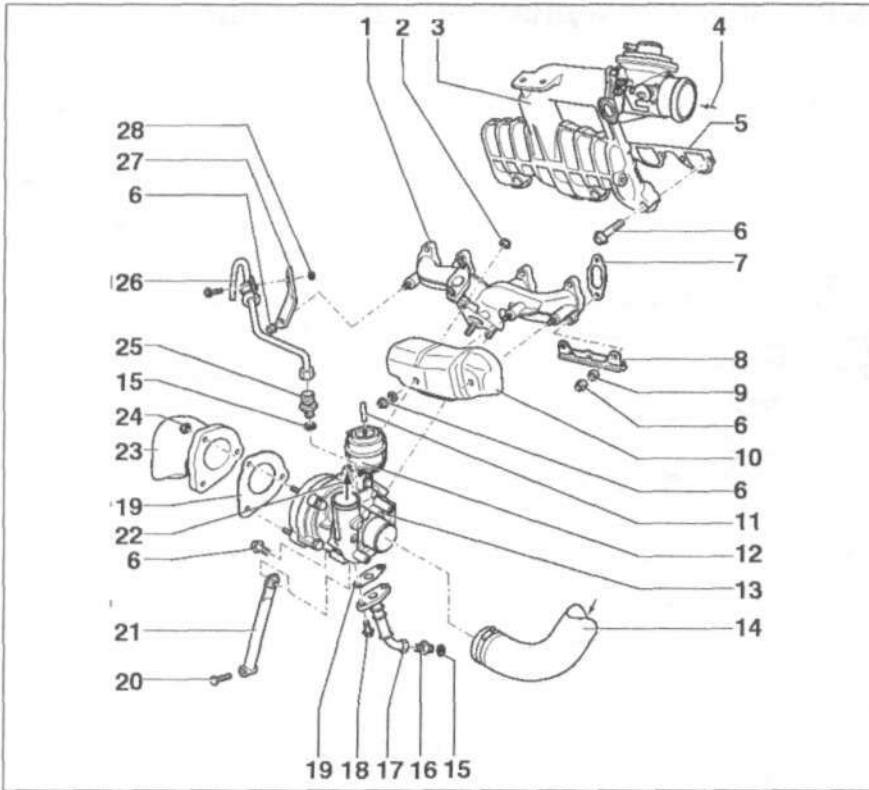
а. Турбокомпрессор с присоединяемыми элементами двигателя AGR:
